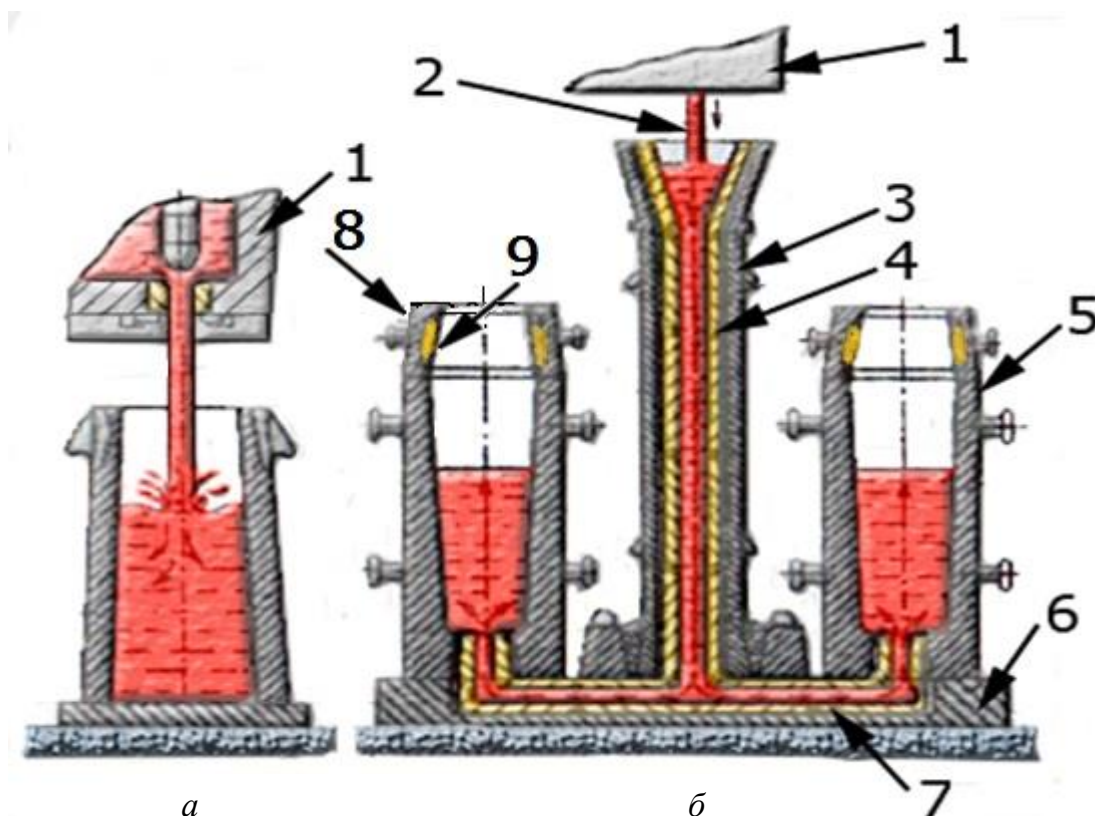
Разливка стали в изложницы: *а* – сверху; *б* – сифоном
